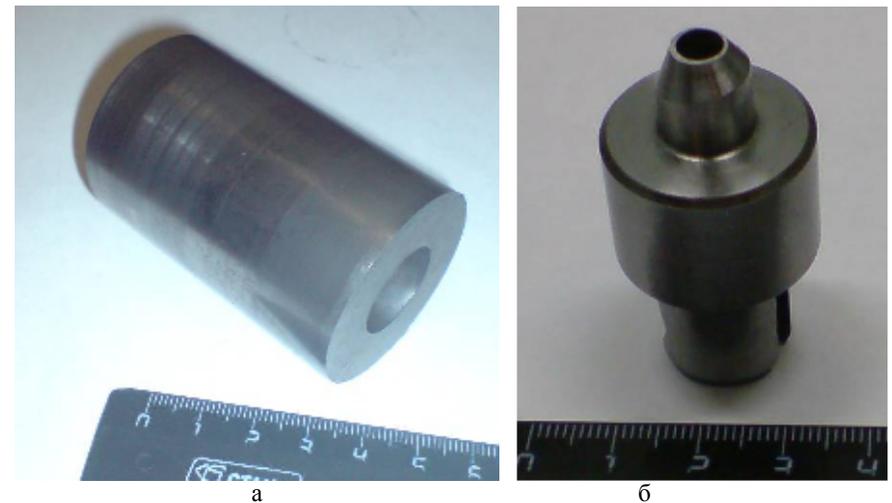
Нож для рубки прутка на заготовки корпуса распылителя (а) и кондукторная втулка для свёрл глубокого сверления топливоподводящих отверстий корпусов форсунок (б)
